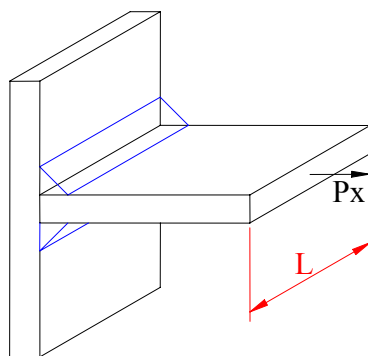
Junta T com a chapa de topo carregada axialmente
